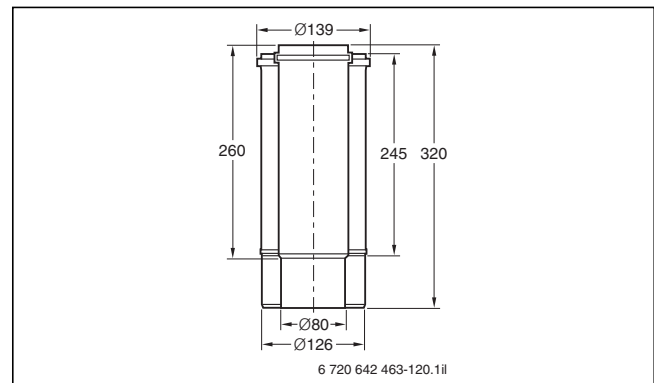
Konzentrisches Schiebestück DN 80/125 (Maße in mm)
